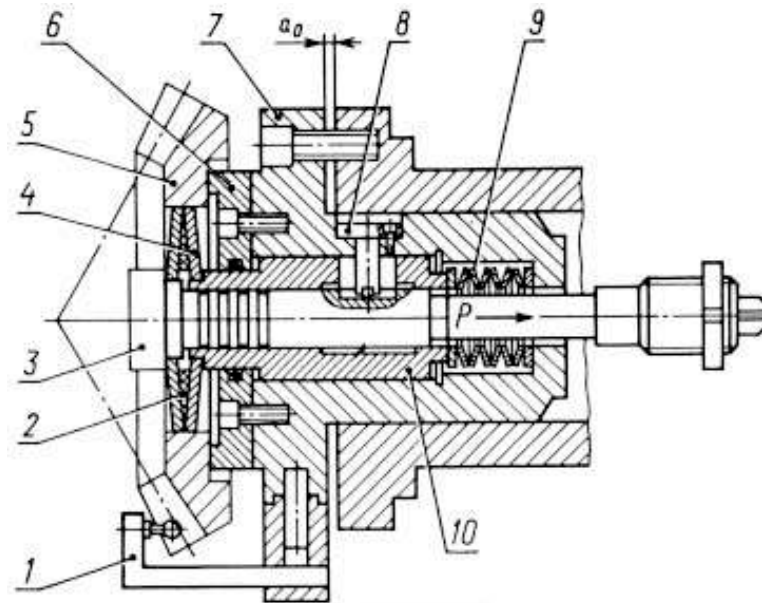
Затискний пристрій для обробки конічного колеса
